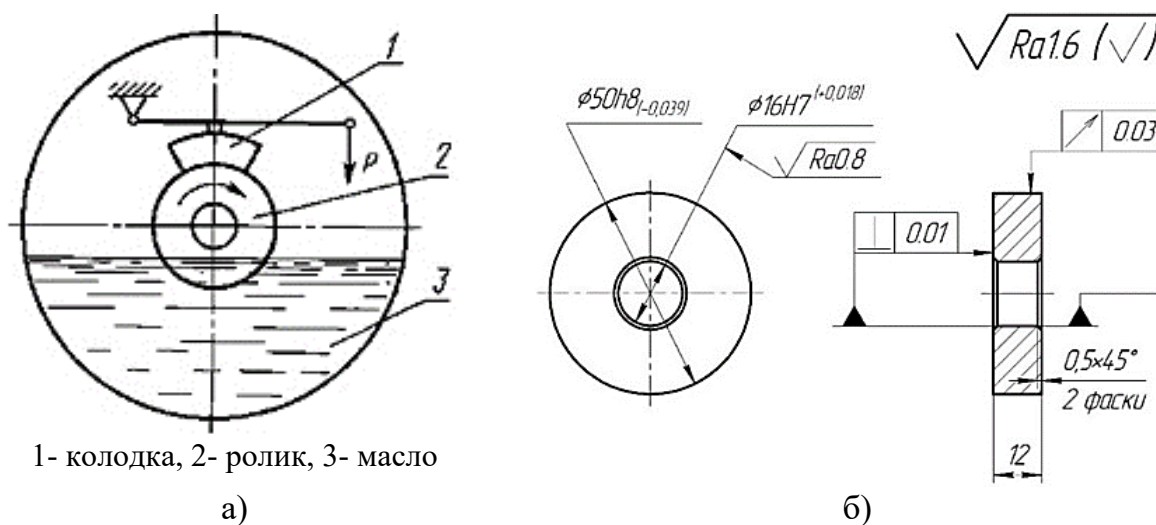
Схема испытаний на износостойкость: а) образцы «колодка - ролик»; б) чертеж стандартного образца
